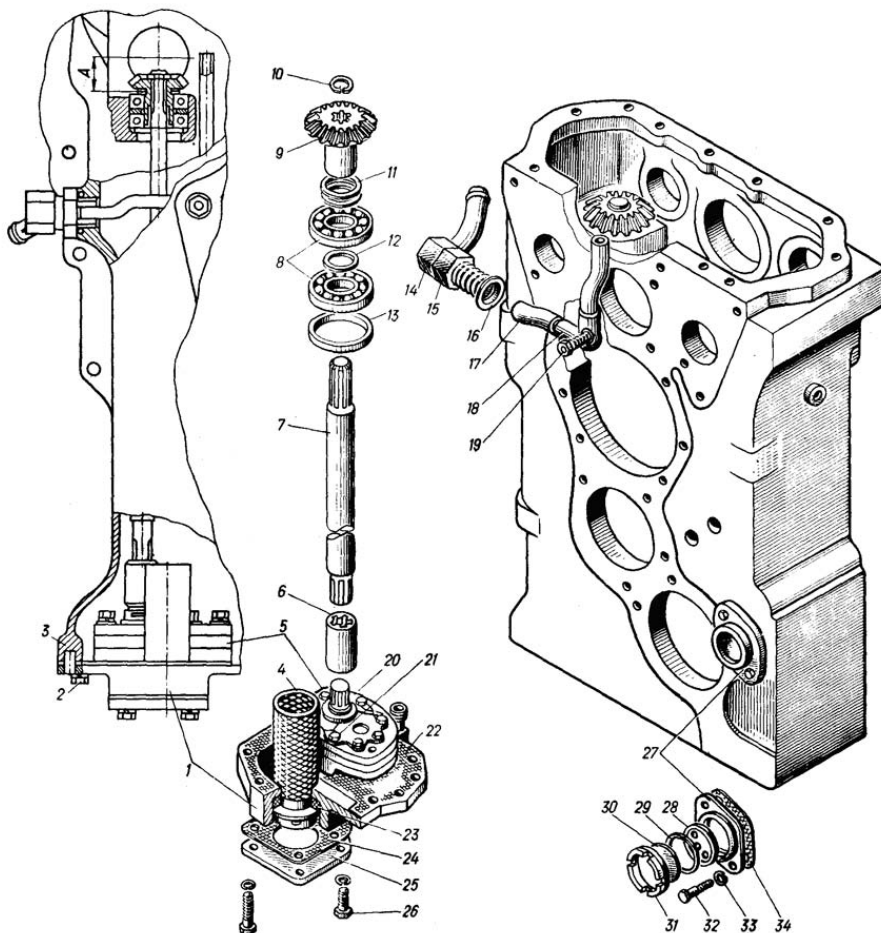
Снятие привода насоса коробки передач: 1, 25, 27 — крышка; 2, 21, 26, 32 — болт; 3 — корпус; 4 — фильтр; 5 — насос; 6 — муфта; 7 — вал; 8 — подшипник; 9 — колесо зубчатое; 10, 11, 12, 13, 16, 23, 29 — кольцо; 14, 18 — штуцер; 15, 19, 31 — гайка; 17 — трубка; 20 — проволока; 22, 24, 34 — прокладка; 28 — экран; 30 — стекло смотровое; 33 — шайба
